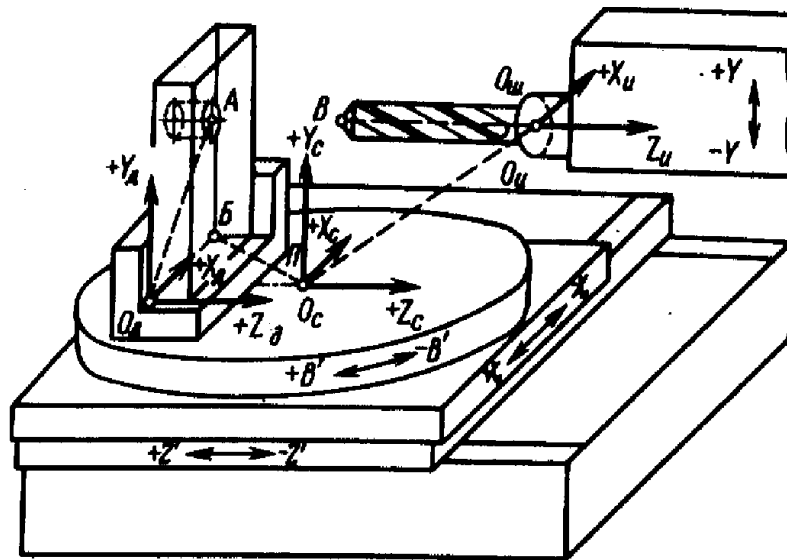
Схема связи систем координат детали и инструмента сверлильно-фрезерно-расточного станка с ЧПУ
